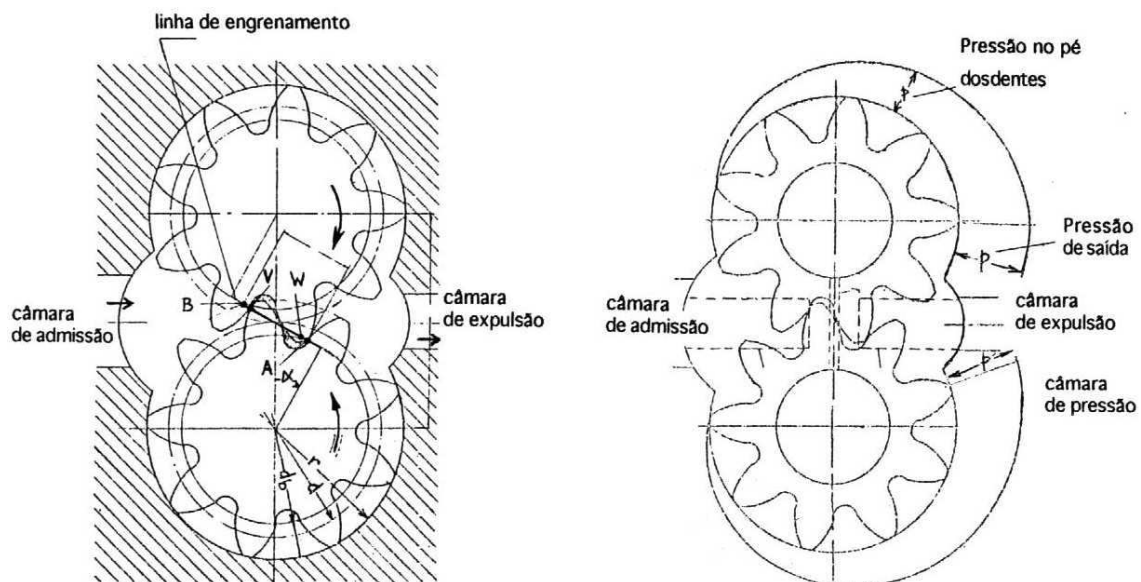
Bomba unicelular de engrenagens exteriores de dentado recto.
